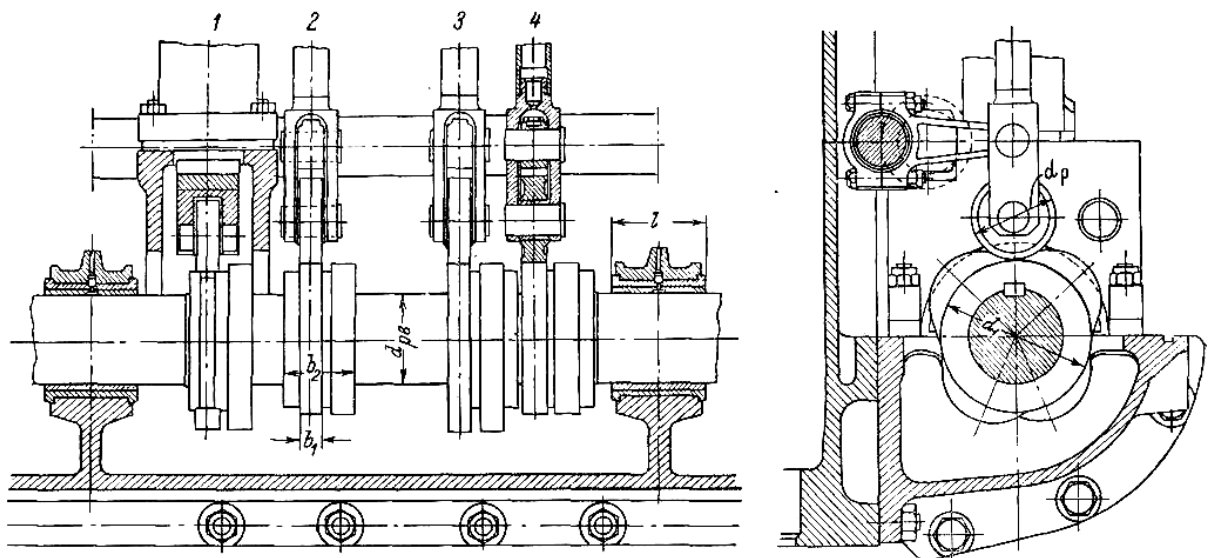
Загальний вид розподільного вала. Привід:
